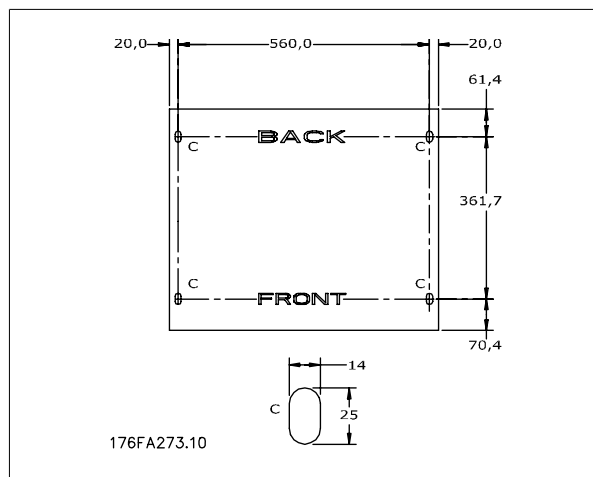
Borekabelon for fastgøringshullerne i gulvet.
